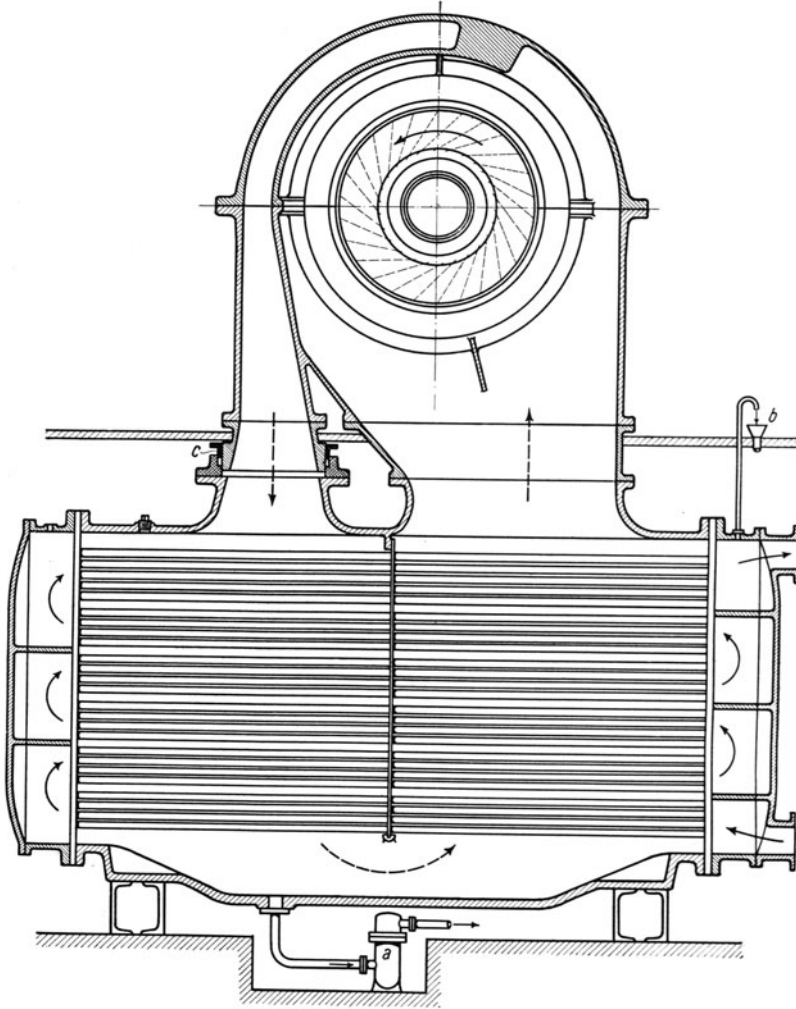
Querschnitt durch einen Turbokompressor mit außenliegendem Zwischenkühler (AEG).
